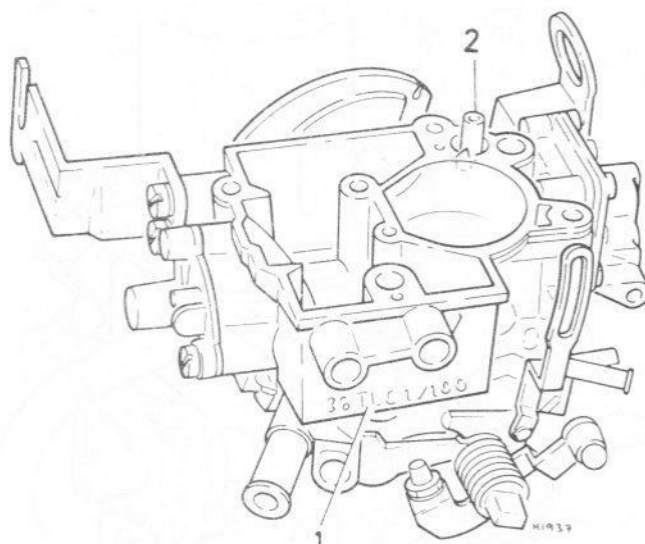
Couvercle supérieur démonté - carburateur Weber 36 TLC (Sec 8)
